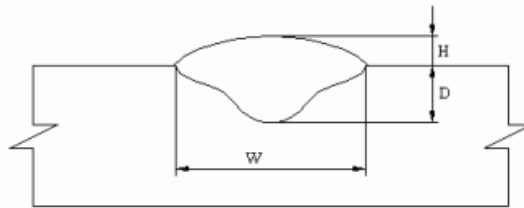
Representação esquemática genérica da soldadura. Largura do cordão de soldadura (W), Profundidade do cordão (D) e Reforço do cordão (H).
